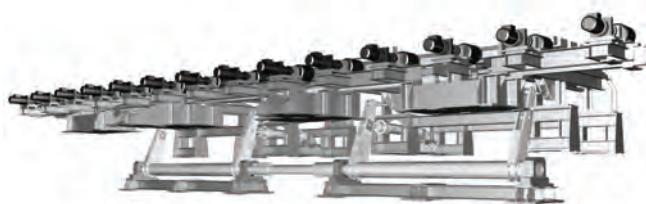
Стол загрузки заготовок перед нагревательной печью
